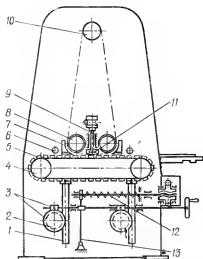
Схема широколенточного шлифовального станка ШЛК8:
